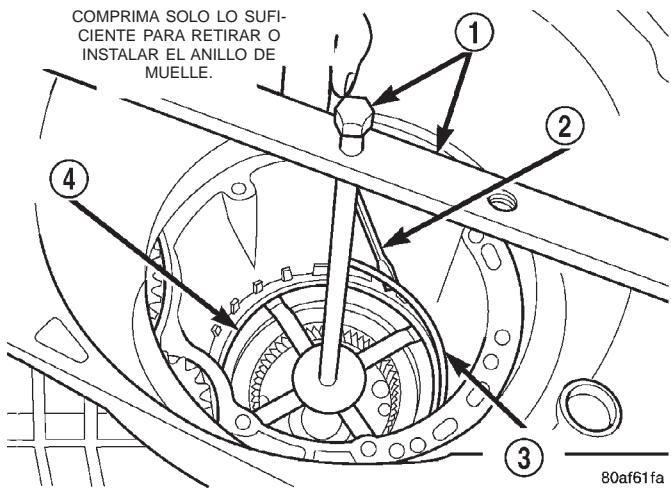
Desmontaje del anillo de muelle del retén del embrague de 2-4
